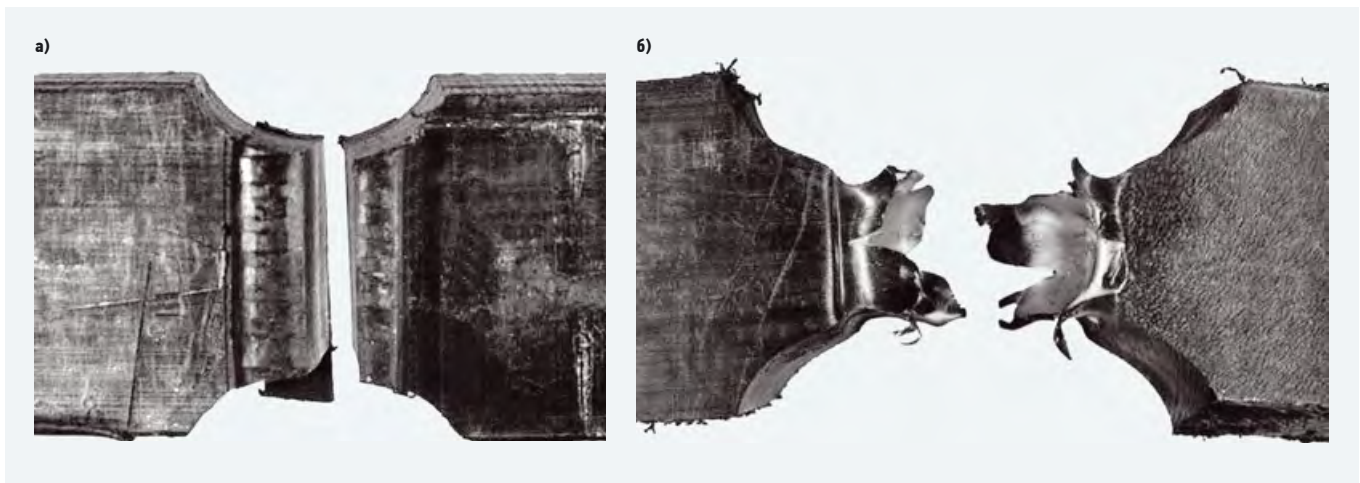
в. Характер разрушения образцов с выточкой при испытаниях сварного шва на одноосное растяжение [а — хрупкое (сварной шов), б — пластичное (материал)]
